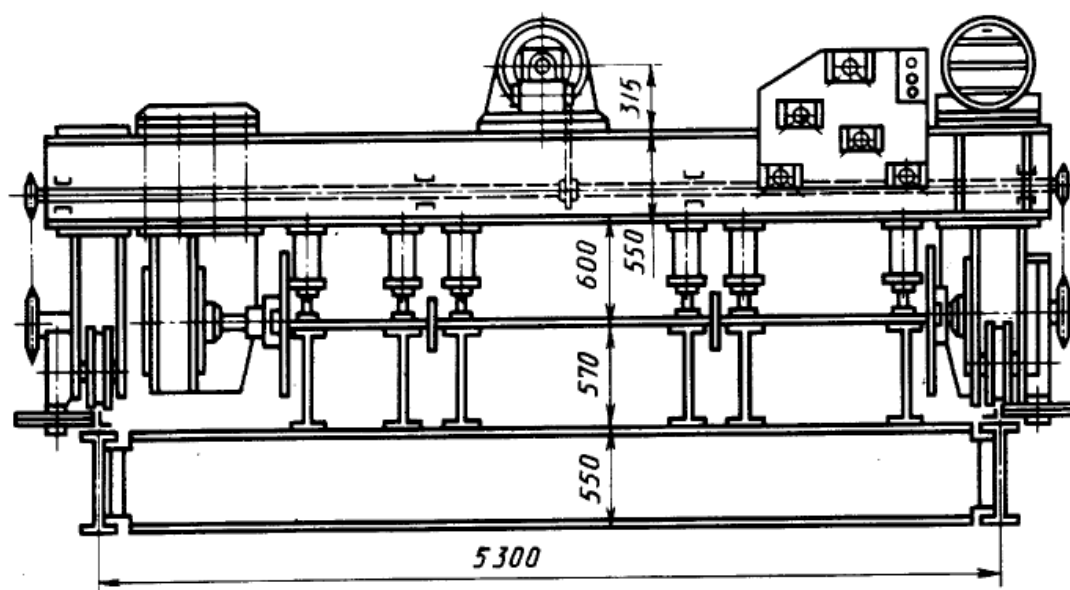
Механизированный универсальный сборочный кондуктор
